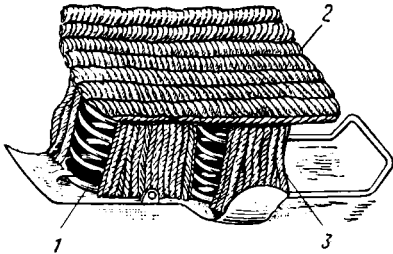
Корпус и крышка объединённой (польстерно-подбивочной) буксы
